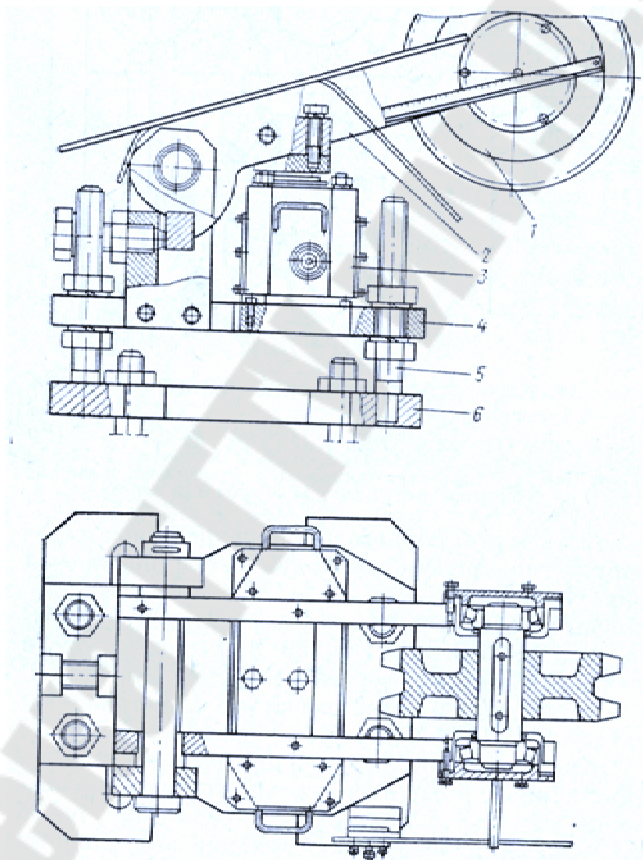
Приспособление ПДМ для установки датчика момента ротора: 1-звездочка; 2- рычаг; 3- датчик; подвижная рама; 5- направляющие стойки; 6-крепежная плита
